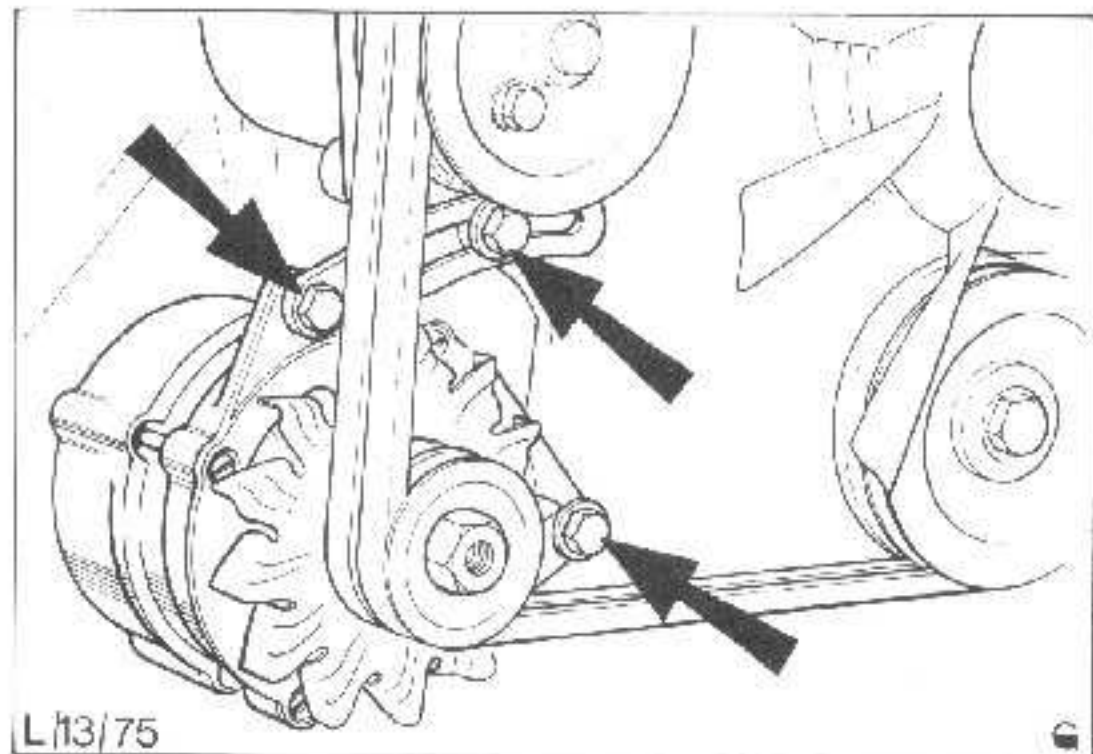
Befestigungsschrauben der Lichtmaschine (DHC-Motor)
